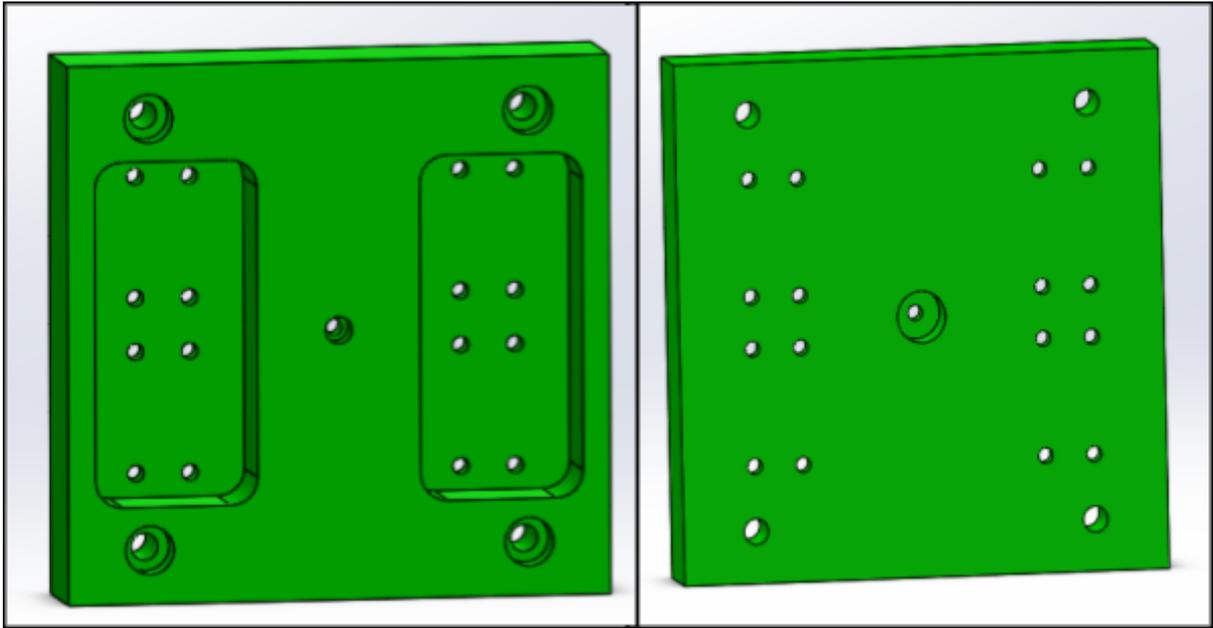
M. Molde de tamaño pequeño de la configuración 3
